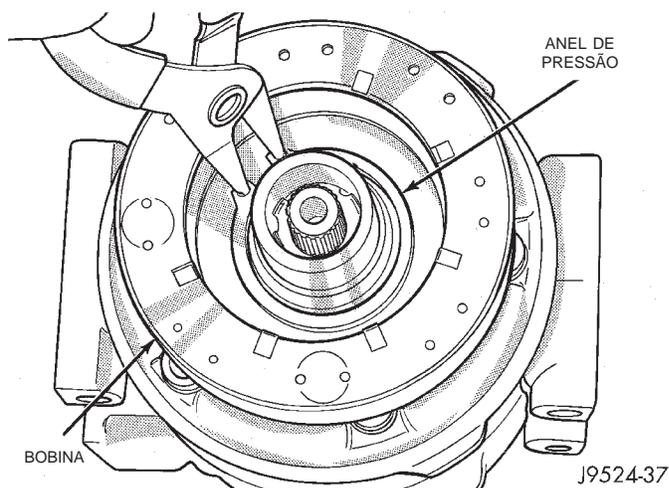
Remoção/Instalação do Anel de Pressão da Bobina do Acoplador
